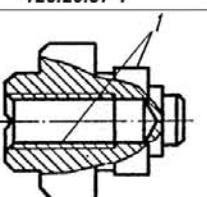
Оправка для напрессовки торцевого уплотнения на шипы крестовины
